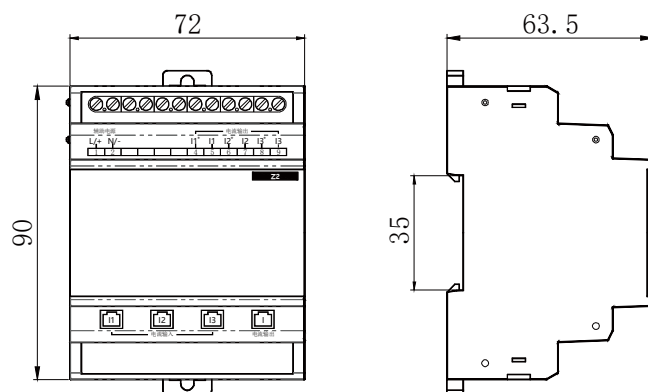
Внешний вид и габаритные размеры модуля коммутации Z2
